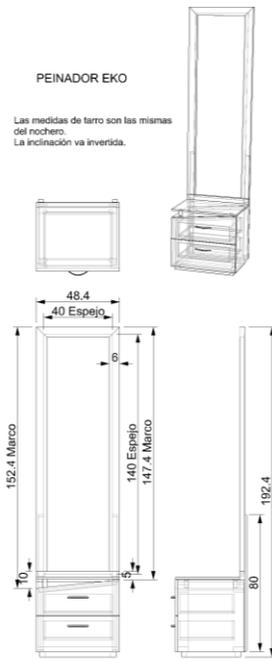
Antecedente Planos y Detalles Técnicos Peinador Eko
